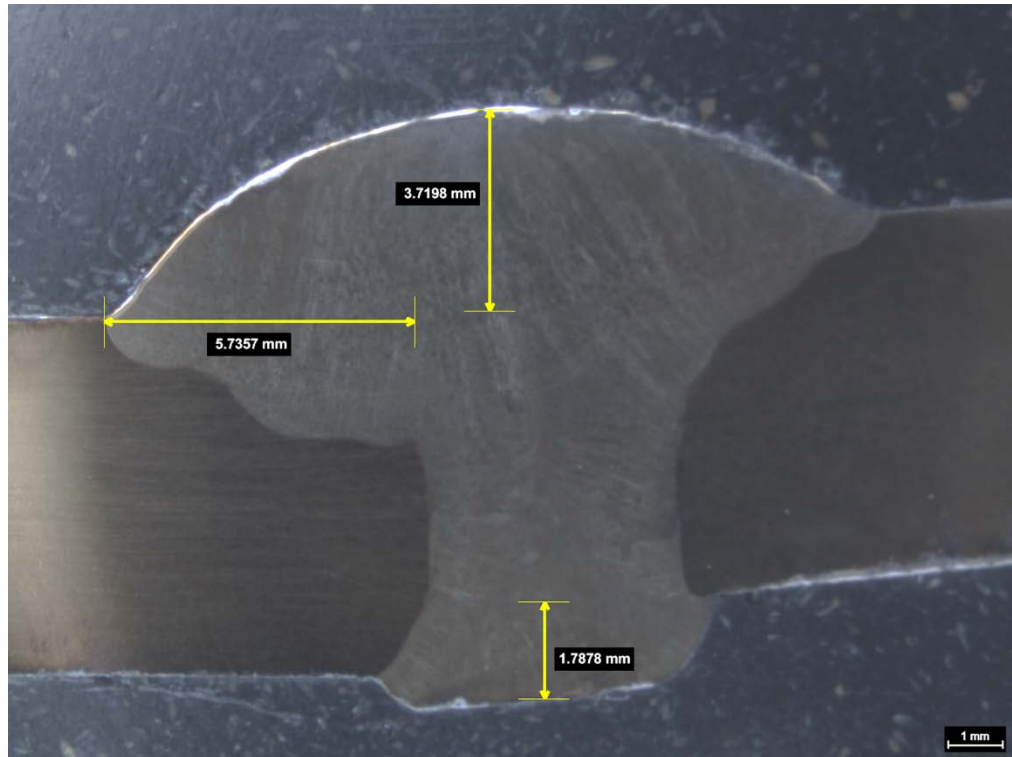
Imagen por macrografía óptica de la soldadura con las dimensiones de las propiedades de la soldadura ER316L.
